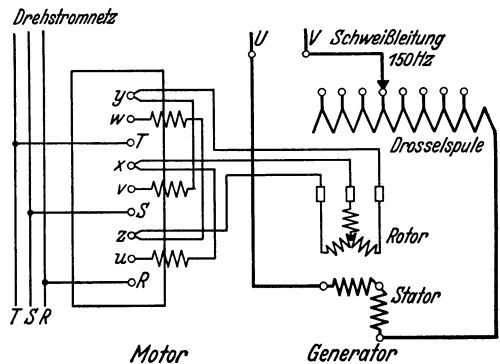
Schema der Periodenumformer-Schweißmaschine.
